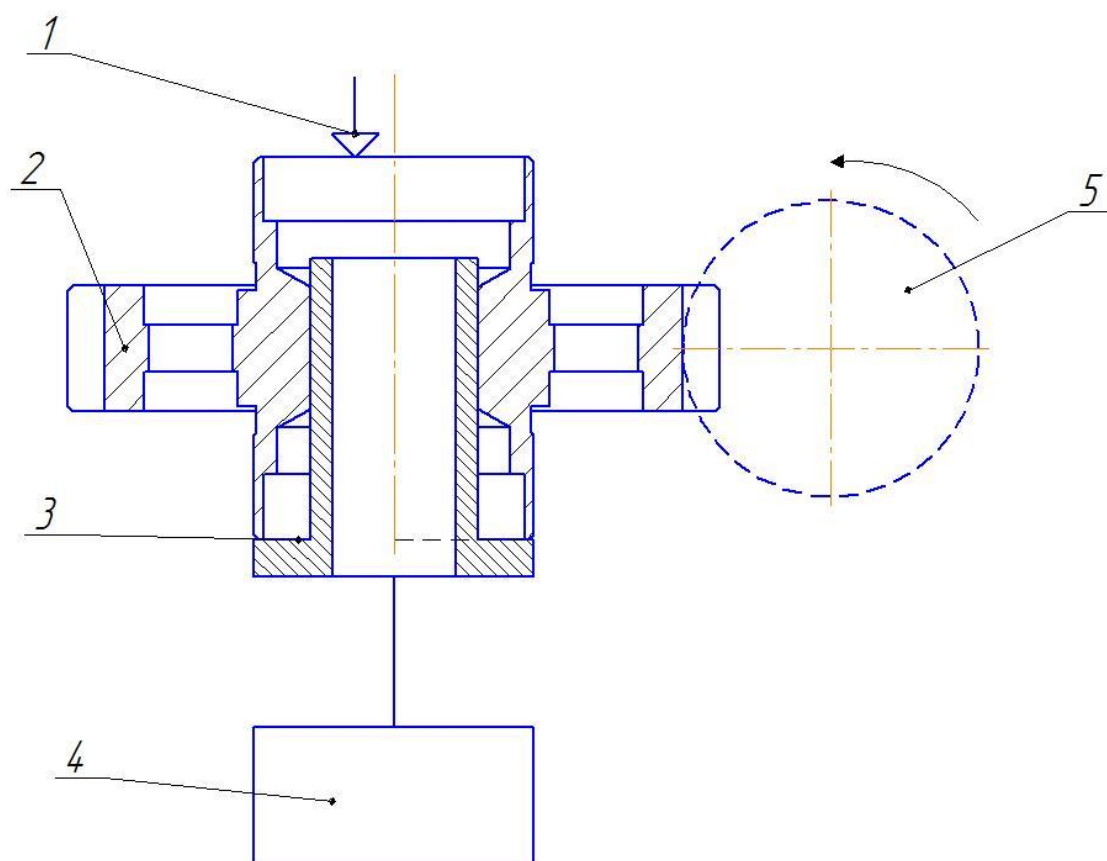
Принципиальная схема приспособления: 1 – установочные элементы; 2 – деталь; 3 – опорная втулка; 4 – корпус приспособления; 5 – фреза.
